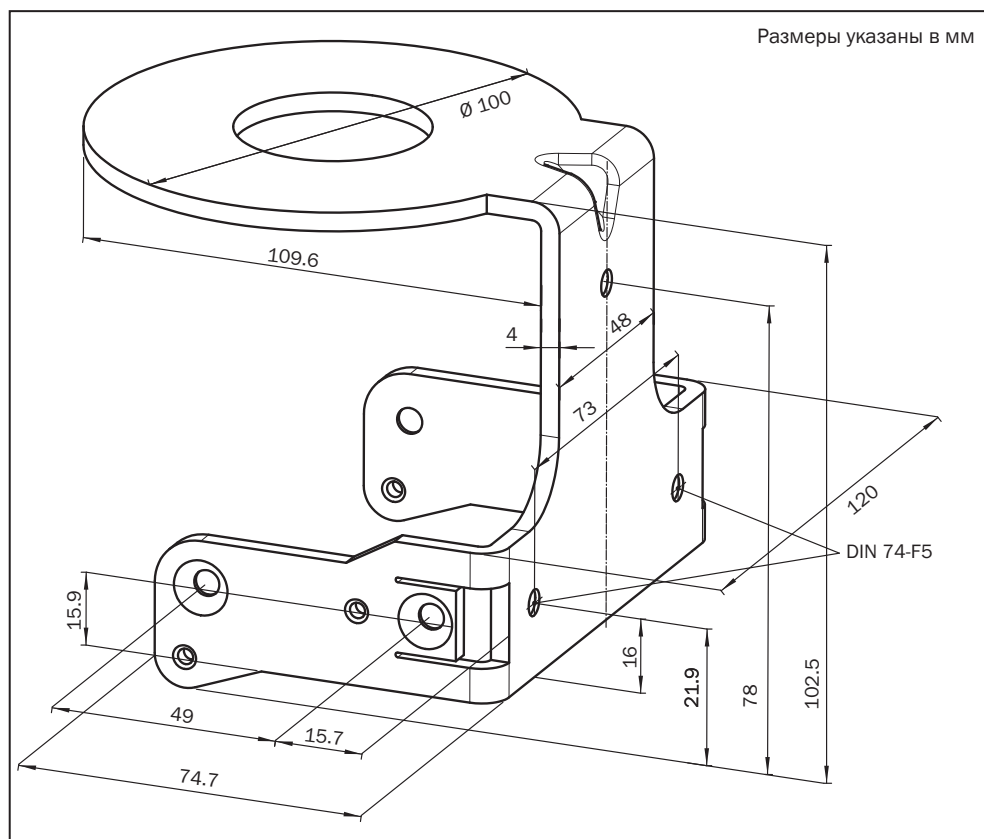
Размерный чертёж монтажного комплекта №16 (Артикул 2034325)
